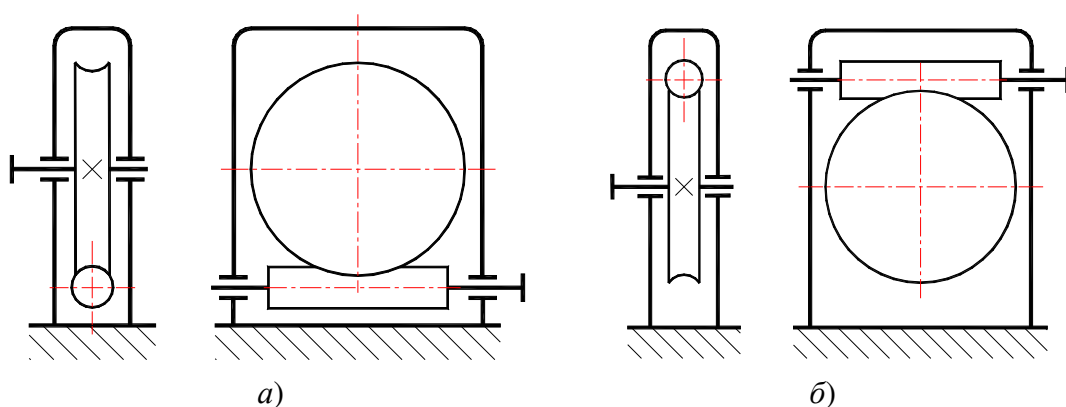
Кинематические схемы червячных редукторов:
